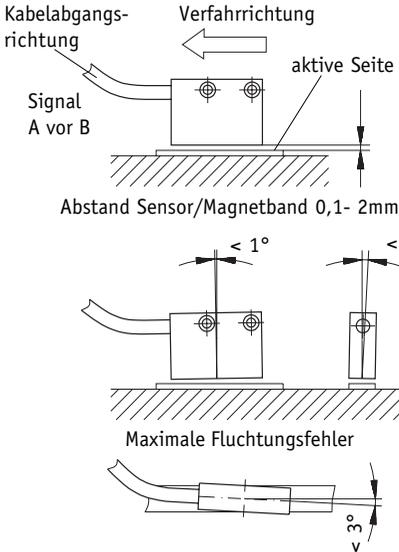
Definition der Zählrichtung mit Magnetband MB... und Montage Sensor / Magnetband, Abstandsmaße, Toleranzen
